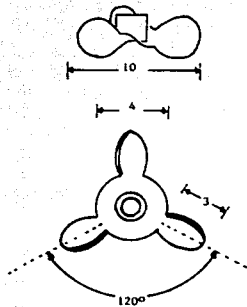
DIMENSIONES DEL IMPULSOR DE HELICE.
